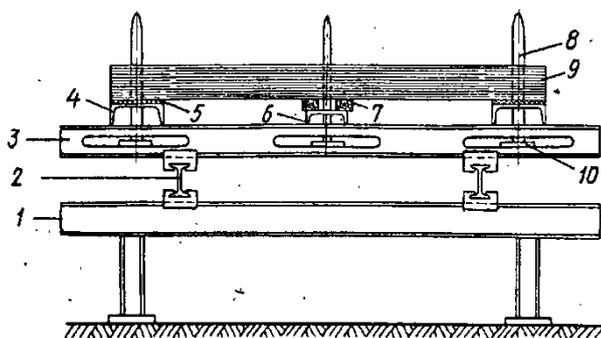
Стол для сборки магнитопровода трансформатора:
